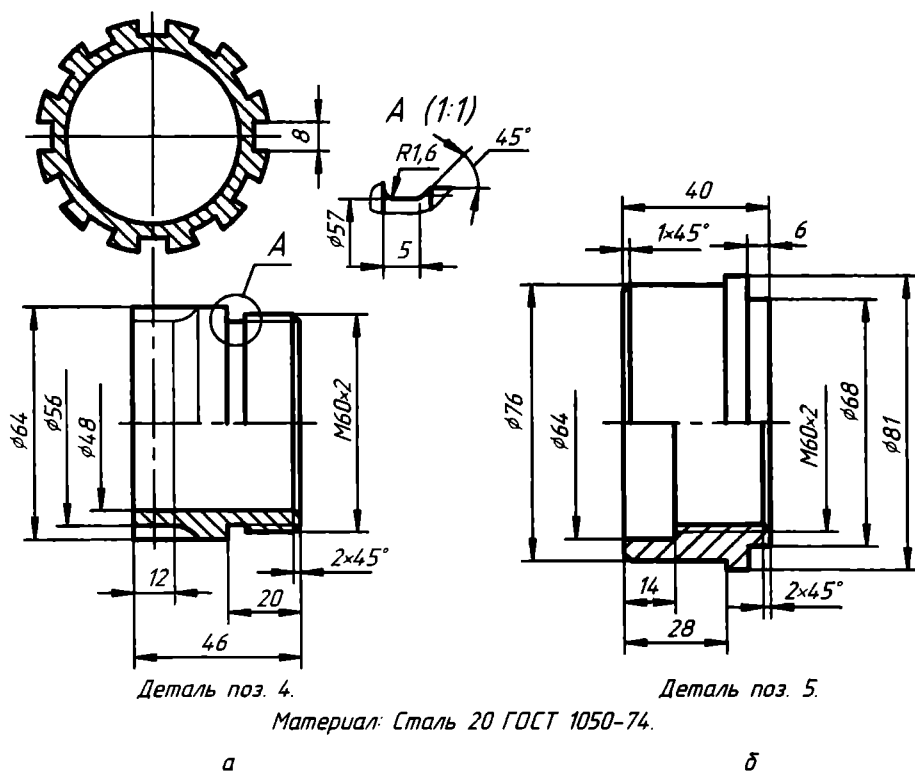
Чертежи: а — гильзы; б — обоймы
